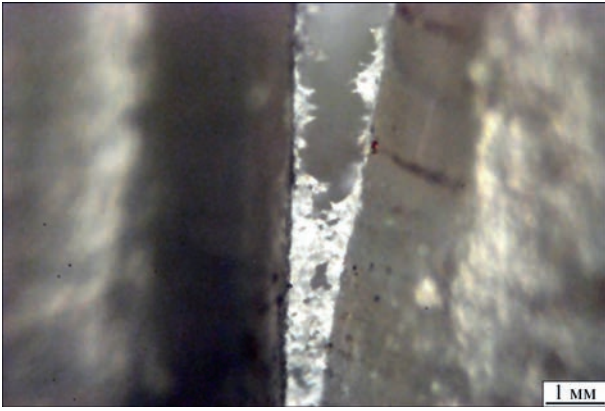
Розвиток тріщини при руйнуванні зварного з'єднання поліетиленових труб, $\times 10$
